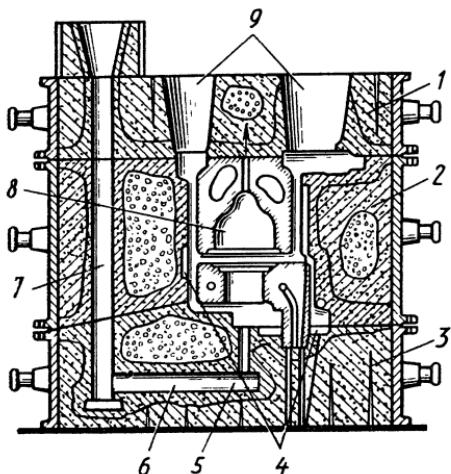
Схема литейной формы для изготовления стальной отливки с применением прибылей и холодильников:
